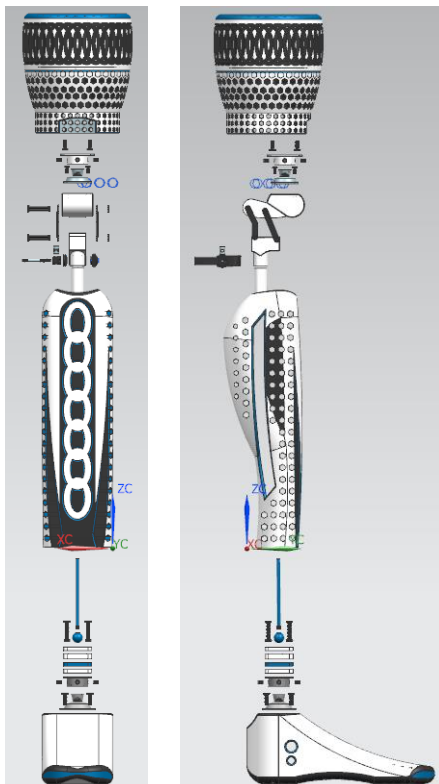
Κίνηση του γονάτου στο Full assembly
